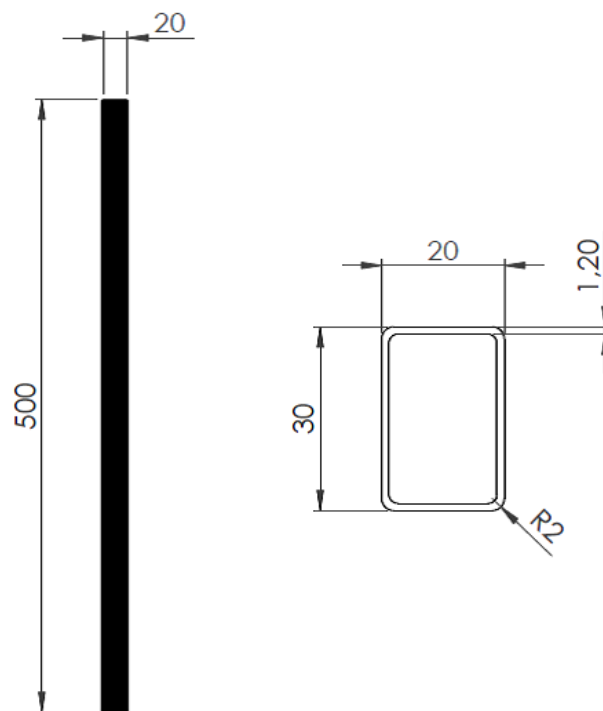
Detalhe dos corpos-de-prova adotados para a aplicação da técnica PIV e modelados pelo Solid Works
